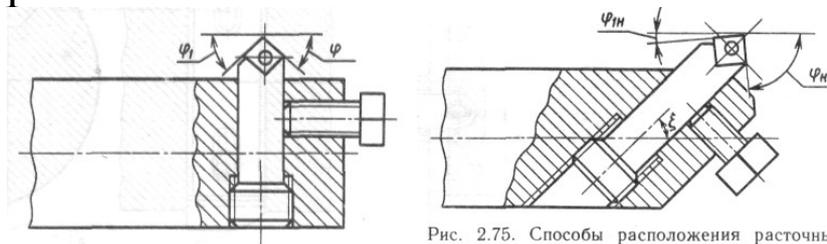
Способы расположения расточных резцов при креплении их в оправках
